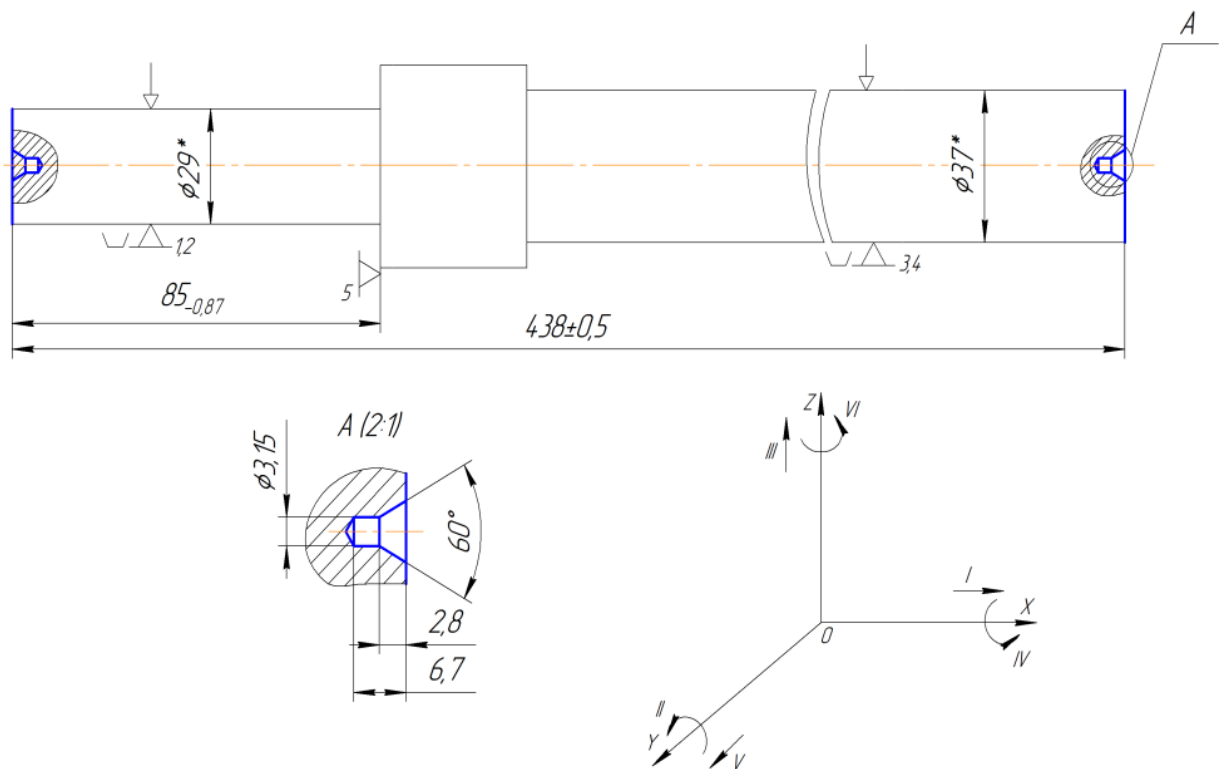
Схема базування деталі для фрезерно-центрувальної операції (варіант 1)
